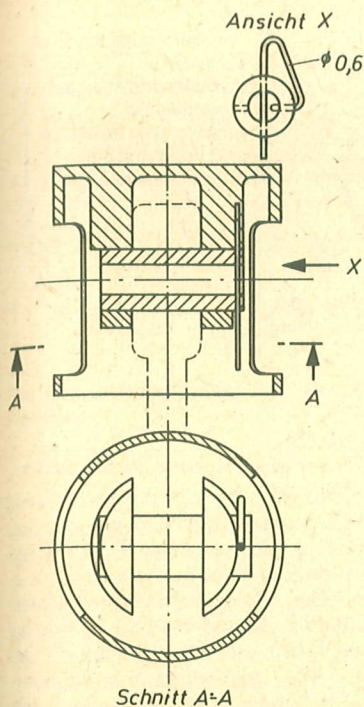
Mit dieser speziellen Kolbenaufhängung kann der gesamte Kolbenmantel für Gasfenster genutzt werden
